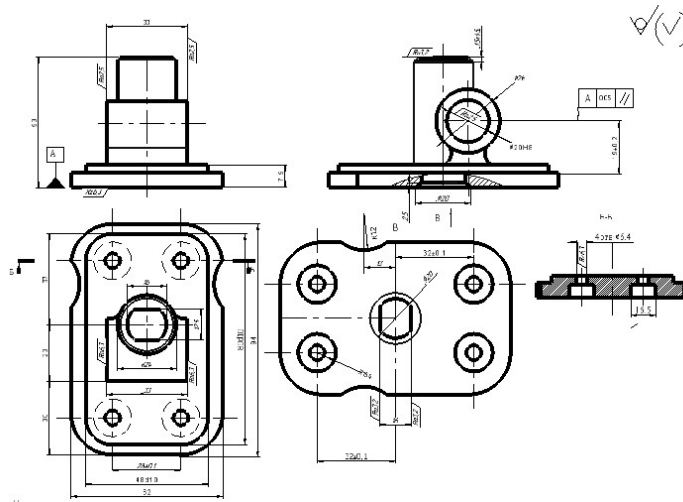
Загальний вигляд деталі «Корпус ДХ.435»
